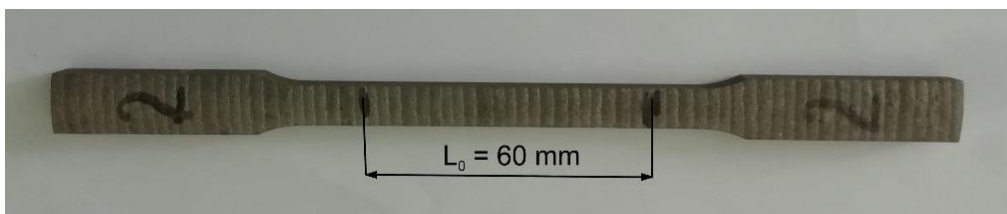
Rozměry vzorků pro zkoušku tahem – jednotlivé vrstvy materiálu.
